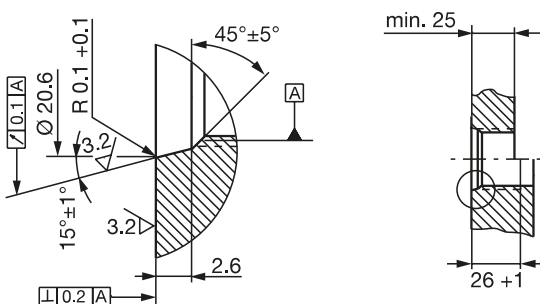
Einschraubloch 3/4"-16UNF nach SAE J475 O-Ring 15.3x2.4
